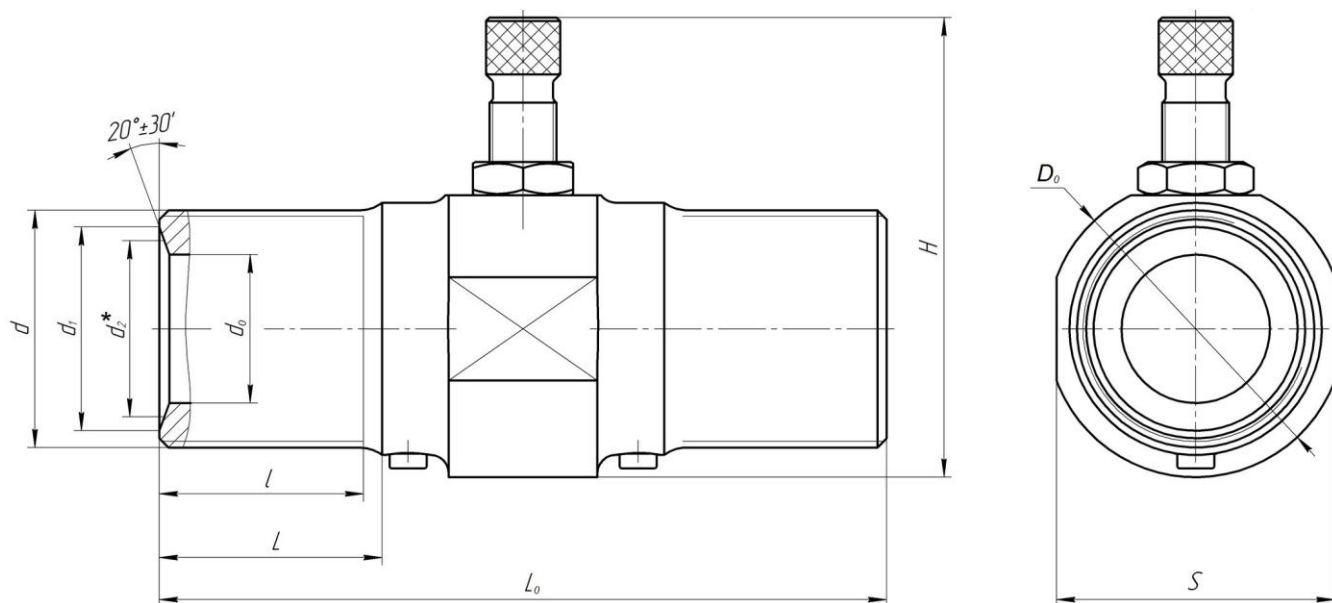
Габаритно-присоединительные размеры ПИП обозначения D
